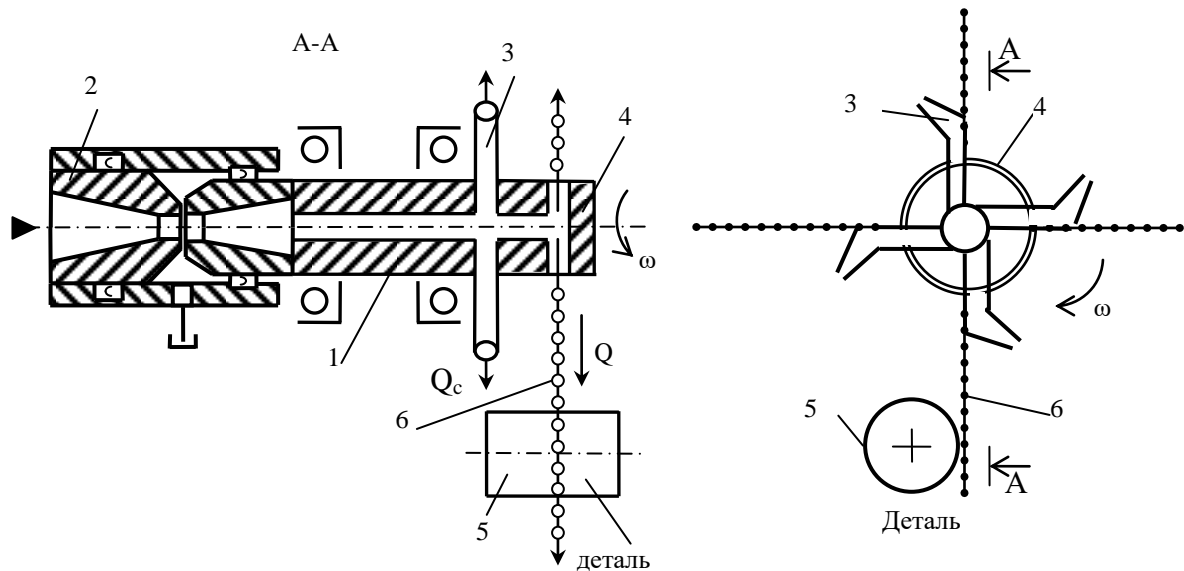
Схема інструменту комбінованої дії для струминно-механічної обробки поверхонь
